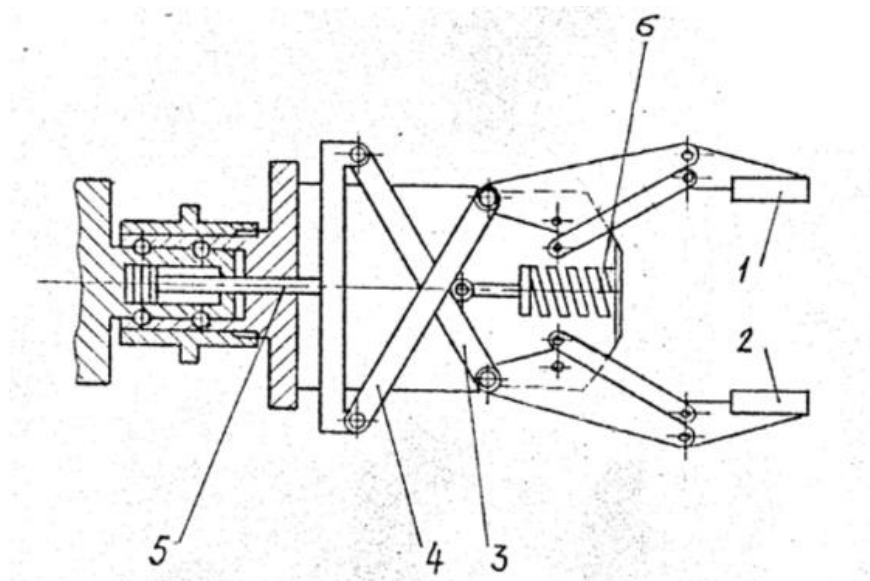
Двухпальцевый схват: 1,2 – пальцы (губки); 3,4 – рычажная передача; 5 – шток пневматического двигателя (пнеумоцилиндра); 6 – возвратная пружина
